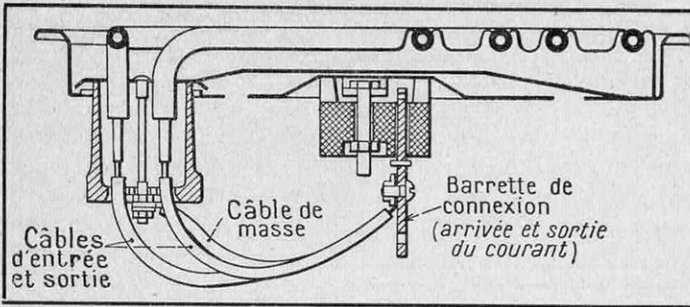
SCHEMA EN COUPE D'UN FOURNEAU ELECTRIQUE ARMÉ D'UNE SPIRE CHAUFFANTE « CALROD »
